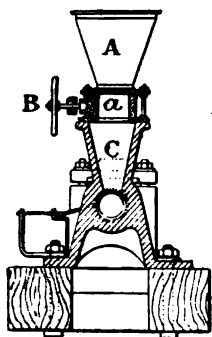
Machine à agglomérer de la Compagnie P.-L.-M.
